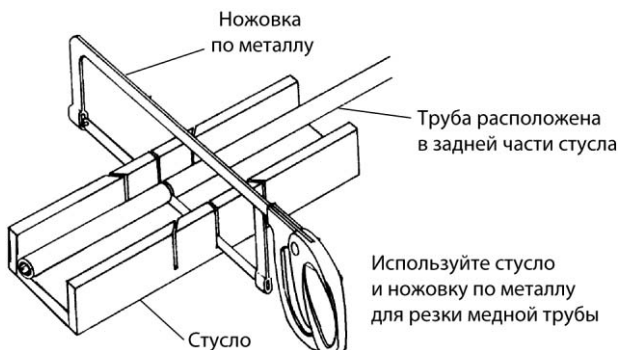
Для резки медных труб могут применяться ножовка по металлу и стусло (приспособление для резки труб)
